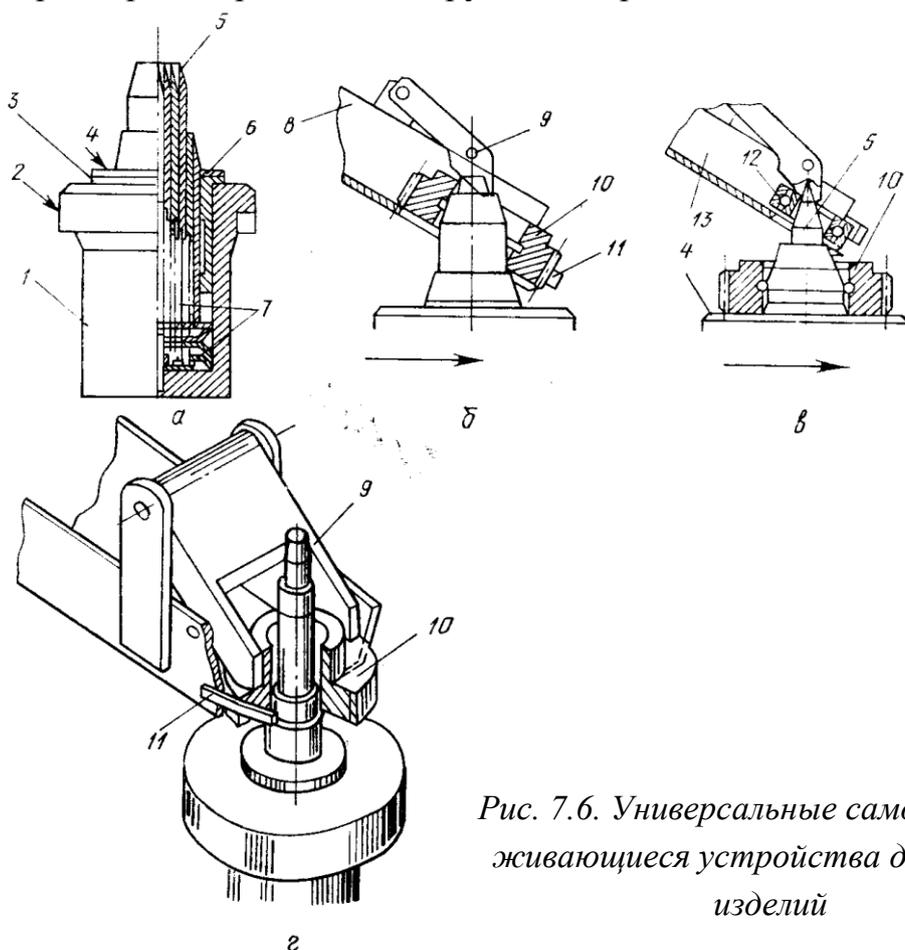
Универсальные самопереналаживающиеся устройства для сборки изделий
